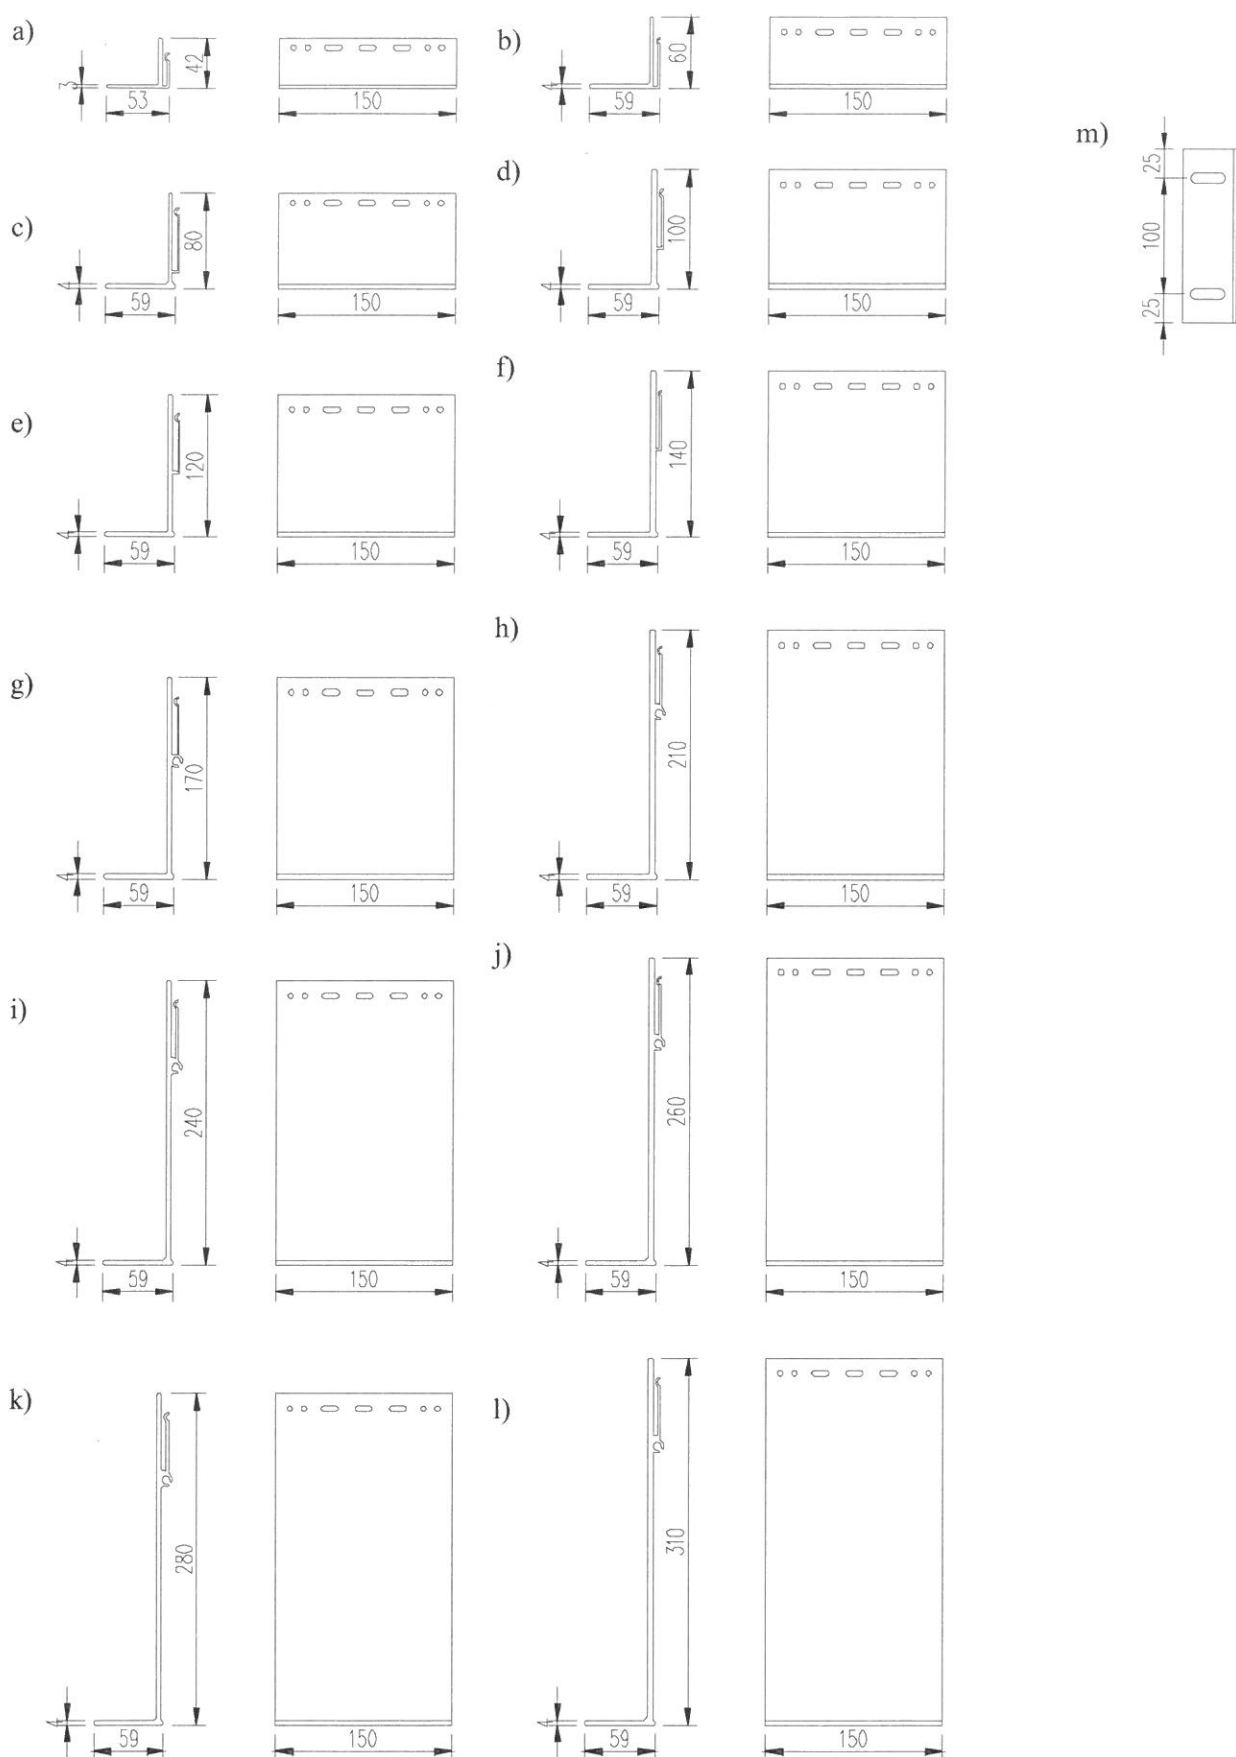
Konsole BSP KW1: a) typ KW1/42-60, b) typ KW1/60-60, c) typ KW1/80-60, d) typ KW1/100-60, e) typ KW1/120-60, f) typ KW1/140-60, g) typ KW1/170-60, h) typ KW1/210-60, i) typ KW1/240-60, j) typ KW1/260-60, k) typ KW1/280-60, l) typ KW1/310-60, m) widok z góry dla wszystkich taki sam
